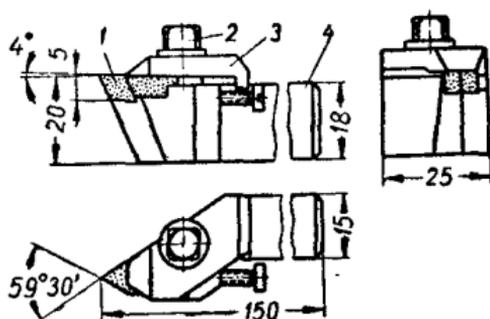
Резьбовой резец с механическим креплением пластинки из твердого сплава конструкции В. М. Бирюкова.
